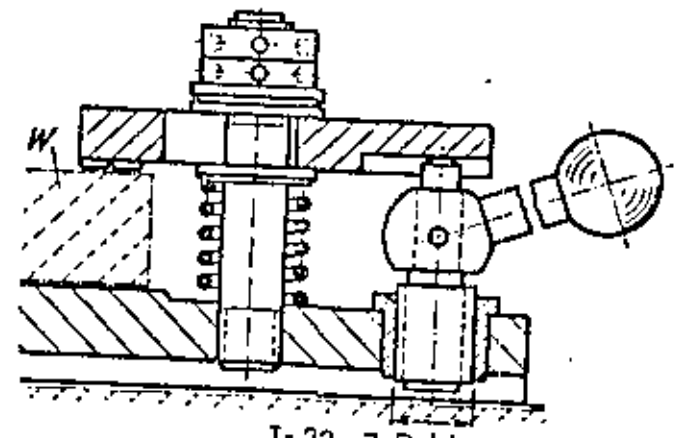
Tensor de coredera con tornillo de apriete con palanca de bola
